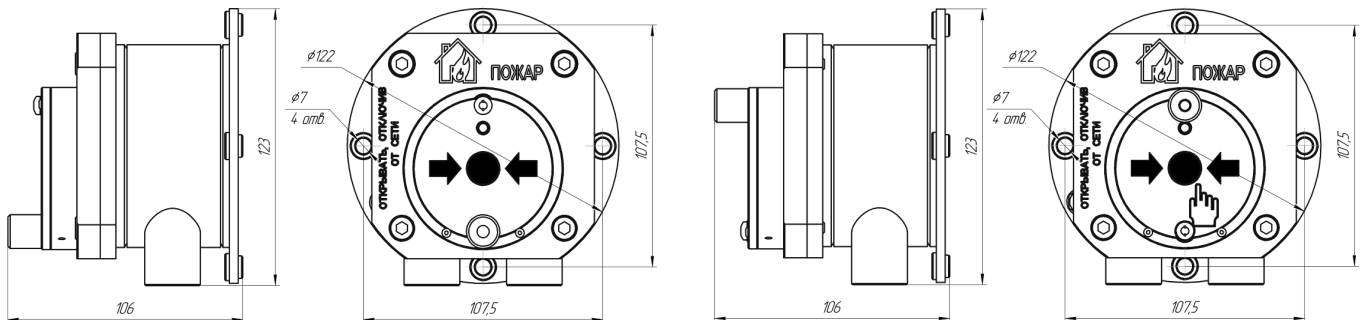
Габаритные размеры ИПР класс А (слева), класс В (справа)
